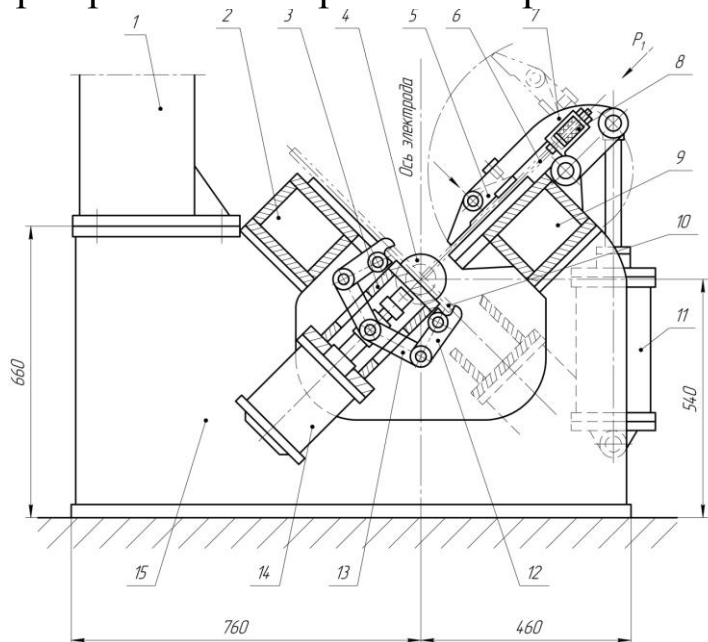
Кондуктор–кантователь для сборки и сварки тавровых балок
